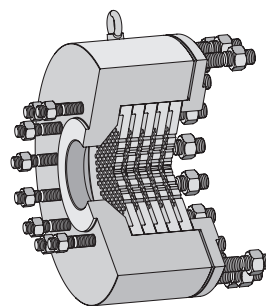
· Tipo 3381-3-5, disegno in sezione con 5 stadi
